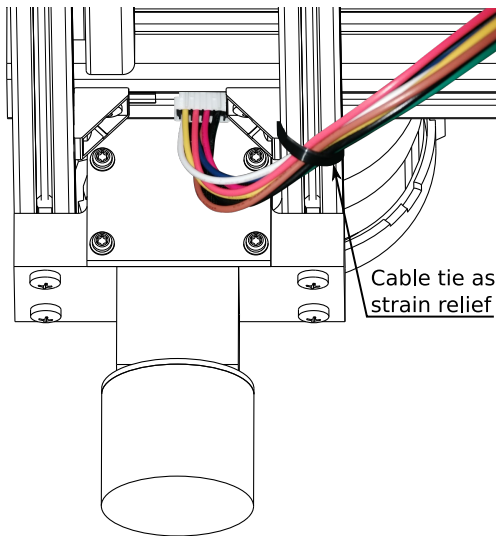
Ein Kabelbinder befestigt das Kabel fest in der Nähe seines Steckers. Das Kabel ist fixiert, was den Verschleiß am Stecker reduziert.
